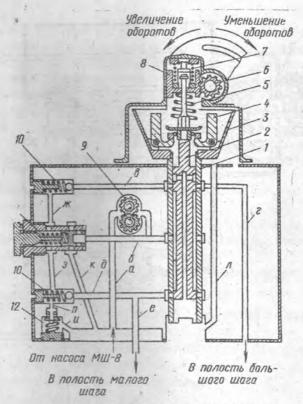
Схема устройства регулятора оборотов Р9-СМ2: 1-возлушный валик; 2-золотник; 3-колокол; 4-Г-образные грузики; 5-коническая пружина; 6-валик ручного управления с шестерней; 7-балансировочная пружина; 8-зубчатая рейка; 9-насос регулятора; 10-шариковые клапаны; 11-редукционный клапан; 12-перегрузочный клапан
